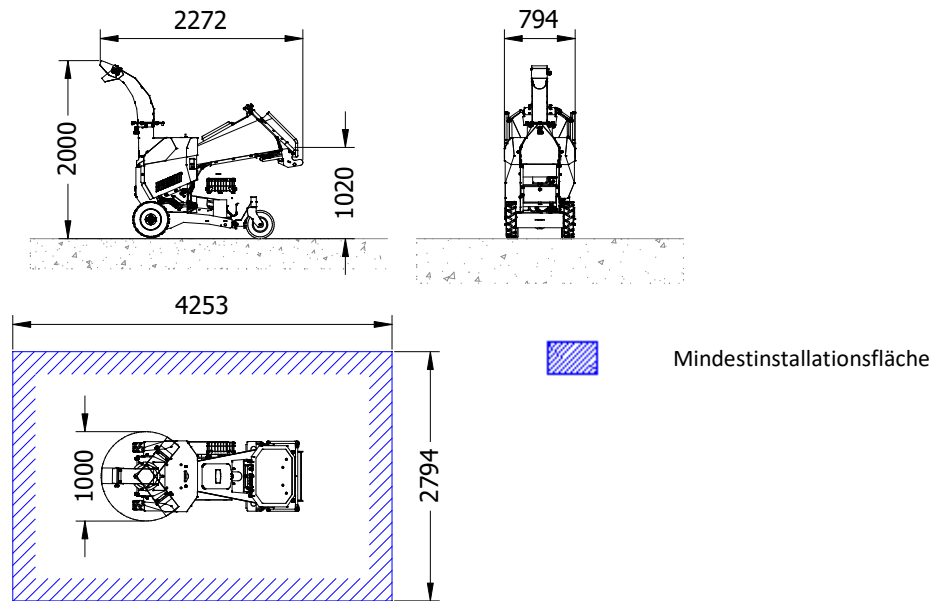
Mindestinstallationsfläche und Maschinenabmessungen
